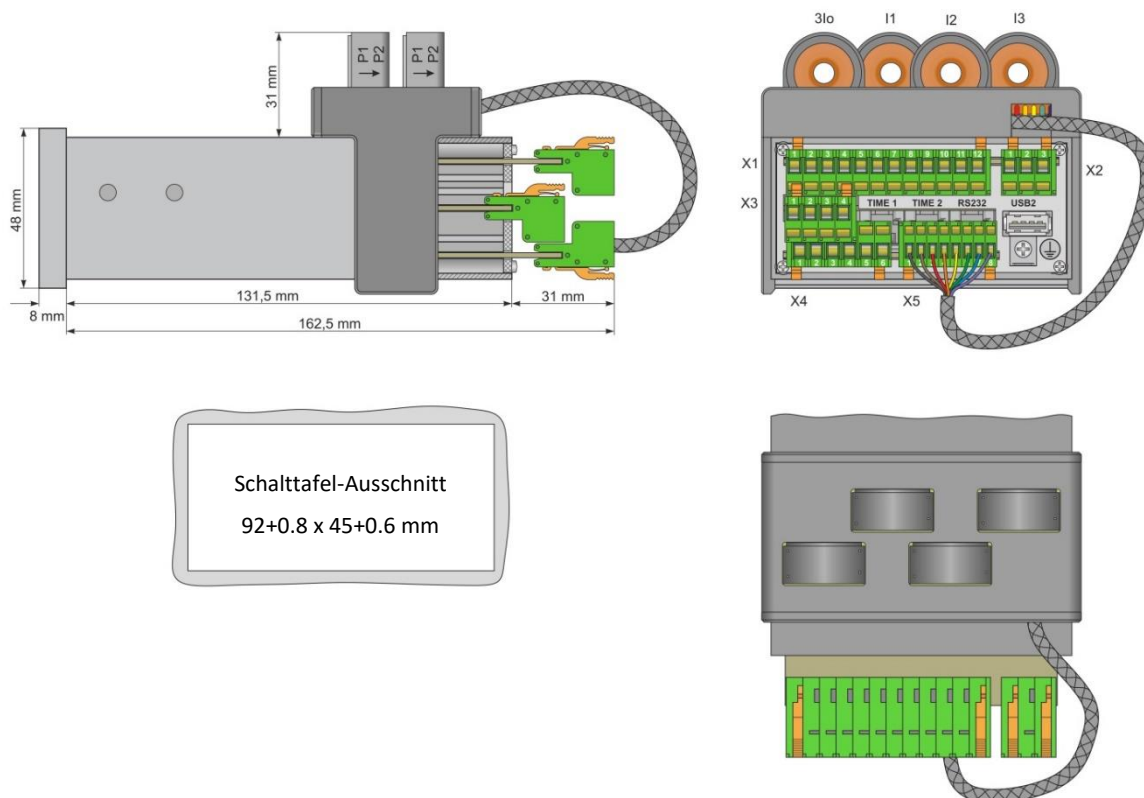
Abmessungen EOR-3D Industriegehäuse und Ansicht von Oben für klassische Wandler
